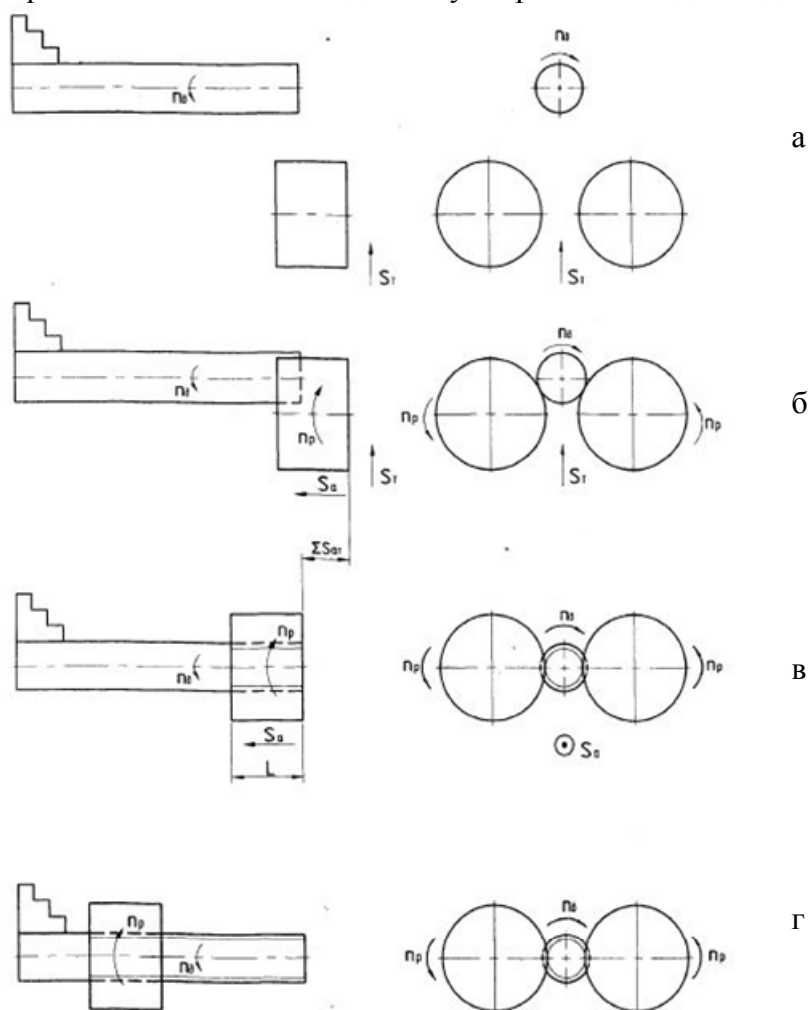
Схема выполнения переходов при накатывании резьбы большой длины:
